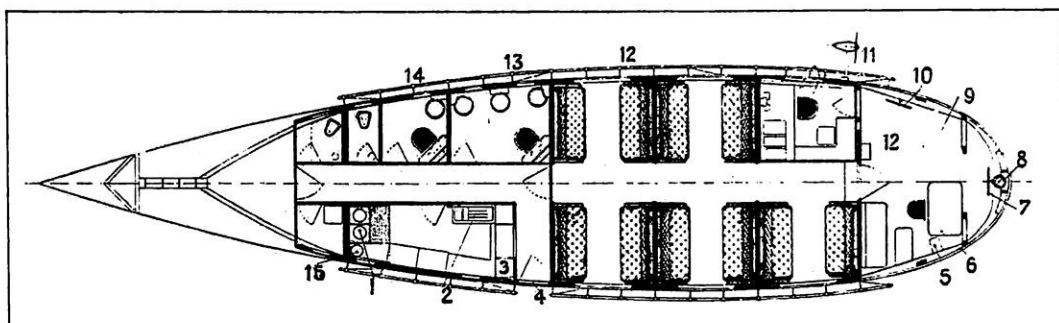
DISPOSITION DE LA NACELLE PRINCIPALE (VUE EN PLAN)
